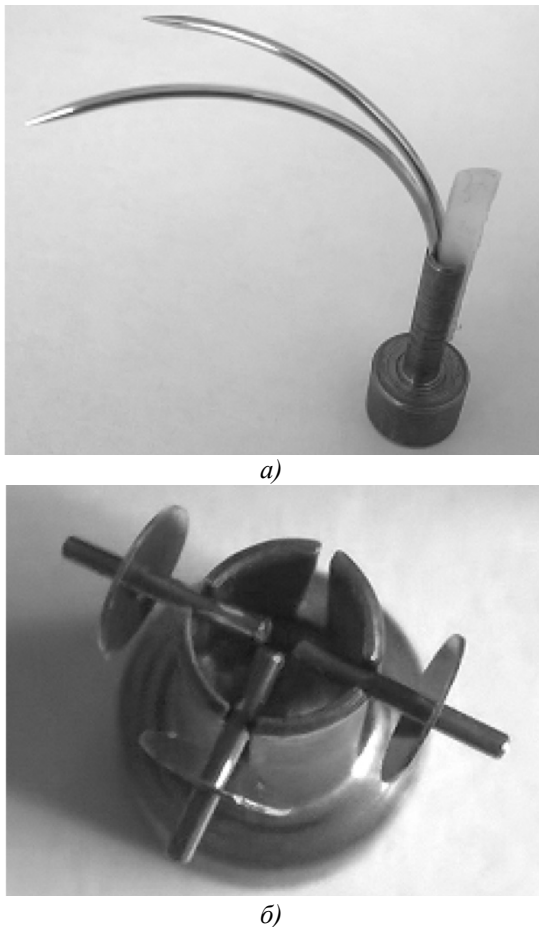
Примеры оснастки для групповой обработки мелкоразмерных заготовок:
